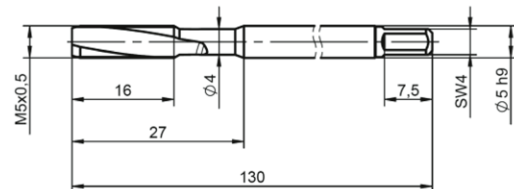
Gewindebohrer M5x0,5 Typ 1357A
